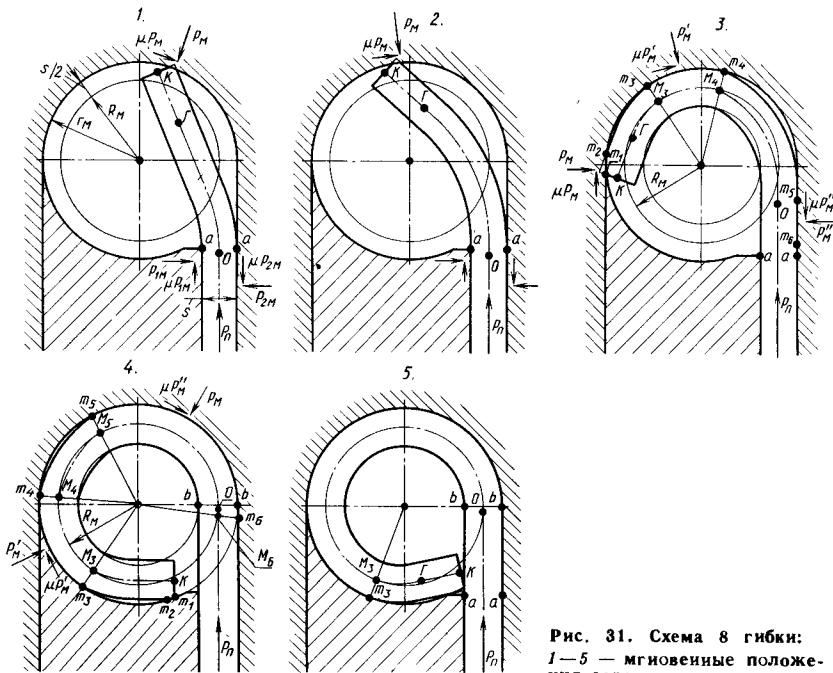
Схема 8 гибки: 1—5 — мгновенные положения заготовки
